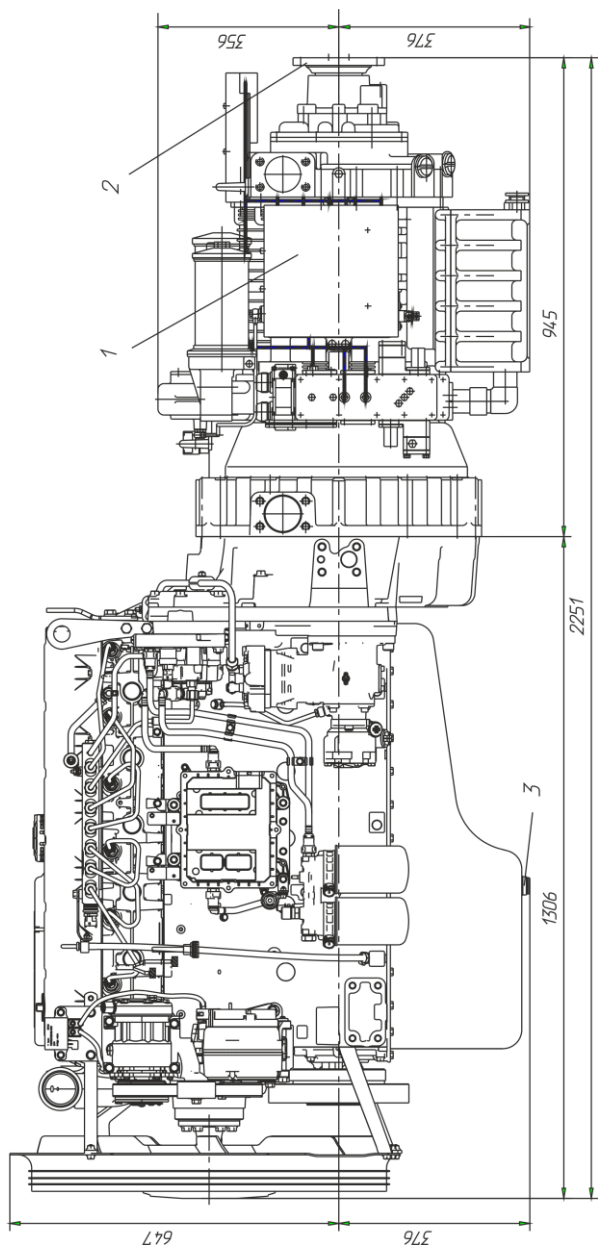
Габаритные размеры силового агрегата ЯМЗ-5367-00:
